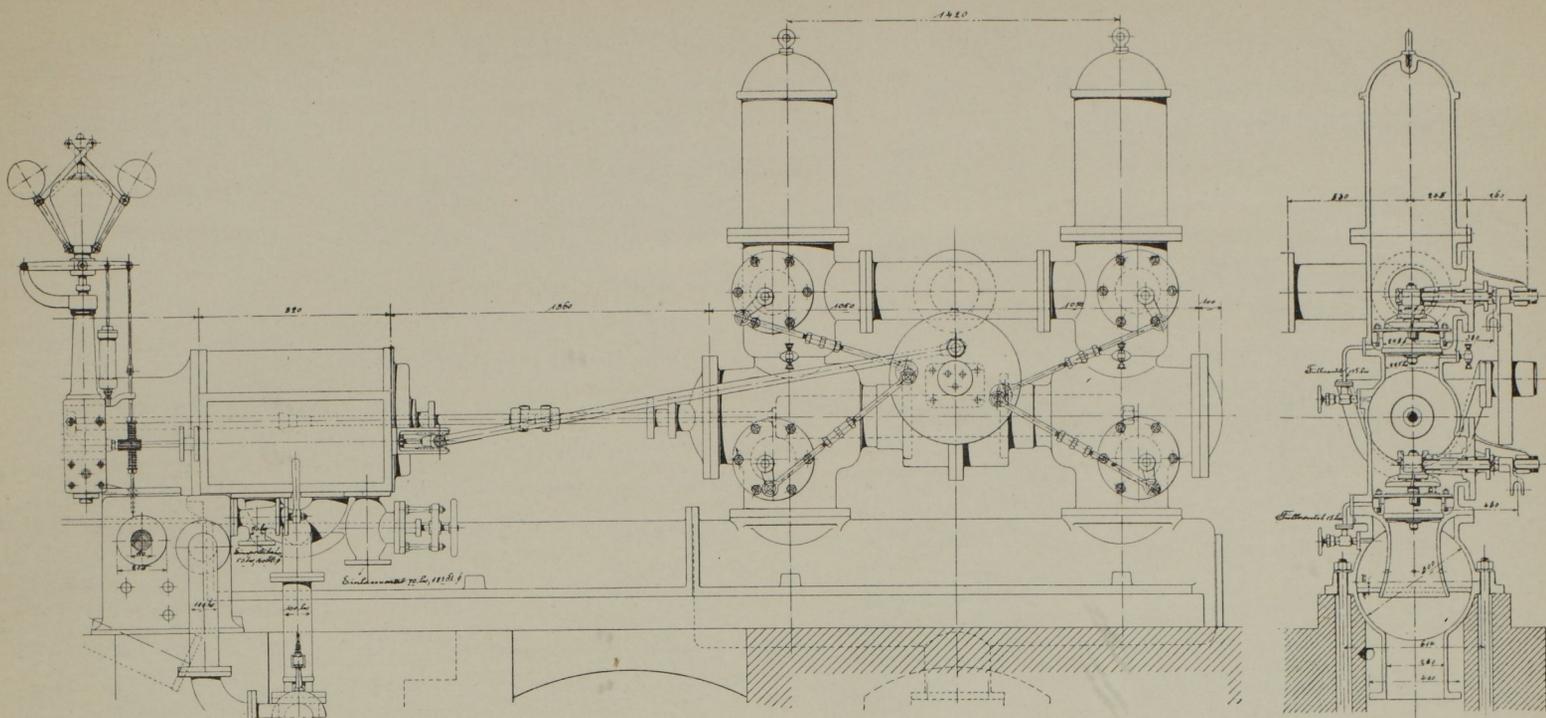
Seitenansicht und Querschnitt der Druckpumpen mit Steuerung. Masst. 1:30.
